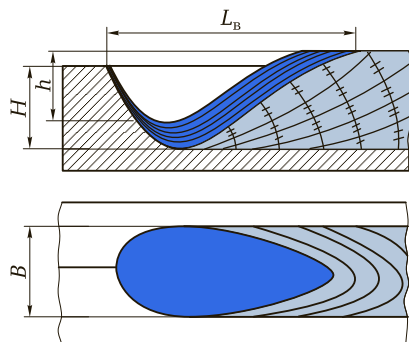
Параметры формы сварочной ванны:
